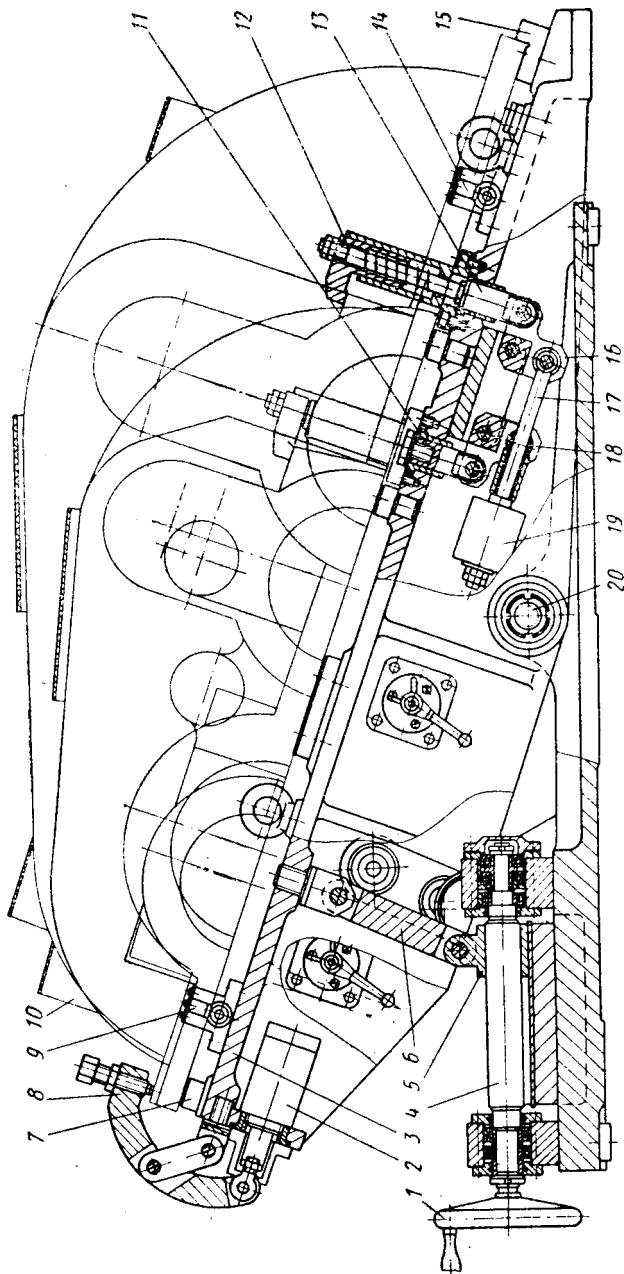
Универсально-наладочное приспособление для закрепления крышек редукторов при фрезеровании плоскостей
